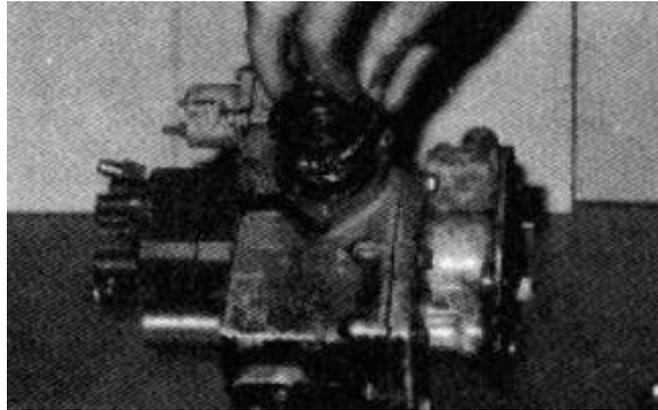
DESMONTAJE DEL ENSAMBLE DEL FUELLE Y EMBOLO DEL AFC
